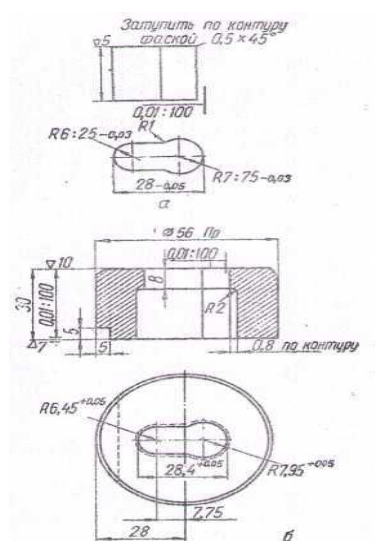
Твердосплавні деталі штампу для планки: а – пробивний пуансон; б - матриця
